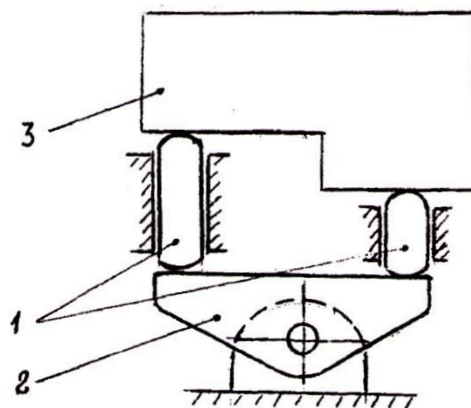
Самоустанавливающаяся опора: 1 – плунжер; 2 – рычаг; 3 – заготовка
